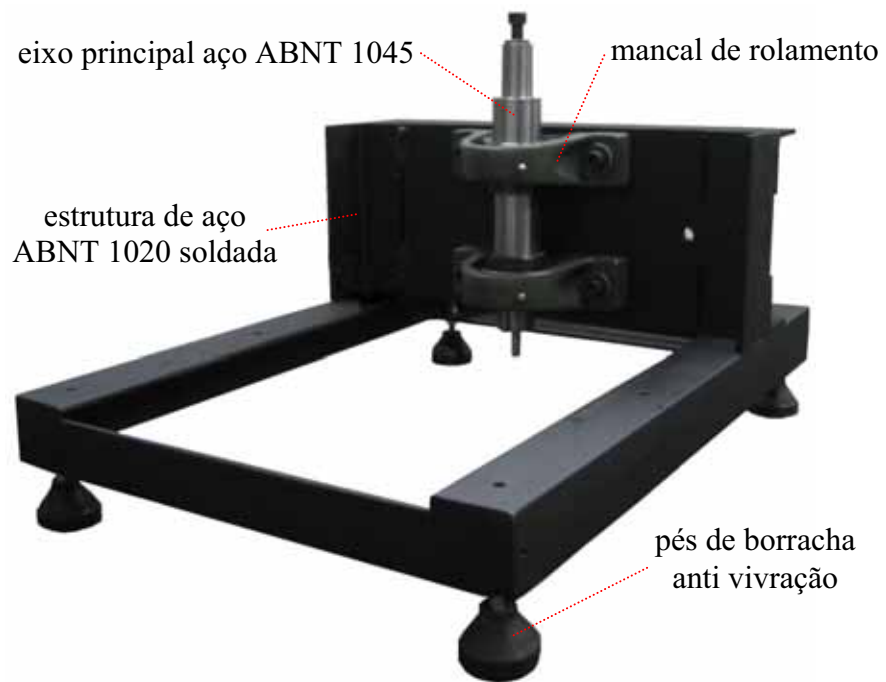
Estrutura da lapidoretificadora: 1ª etapa da montagem.
